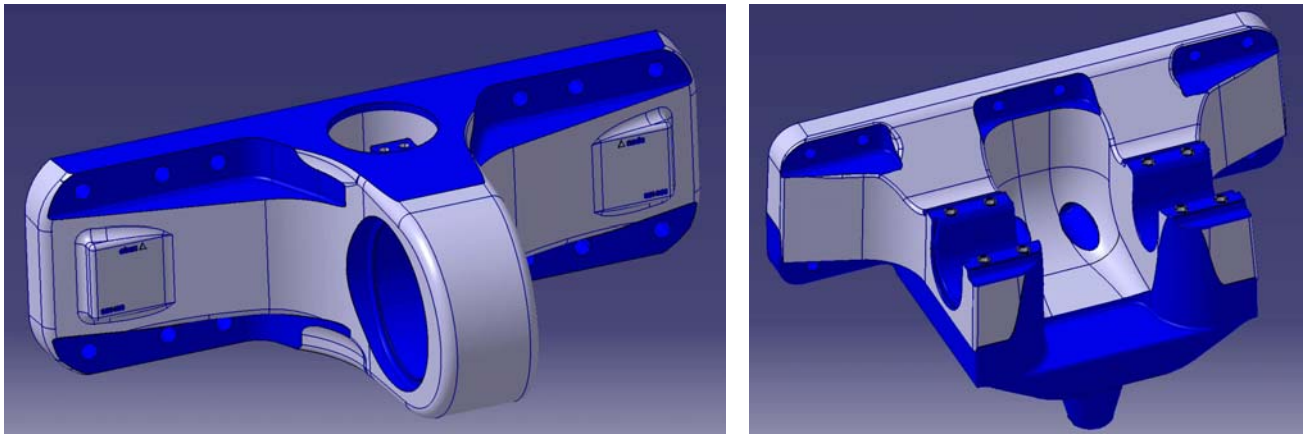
Blau: bearbeitete Flächen, grau: im unbearbeiteten Schmiedezustand belassene Oberflächen
